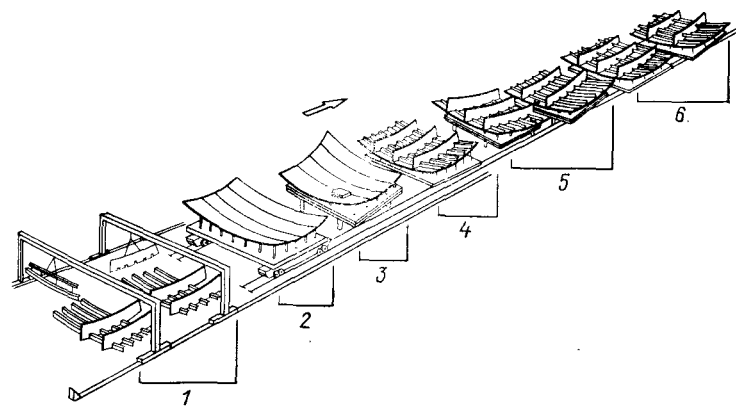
Схема линии сборки и сварки криволинейных секций:
